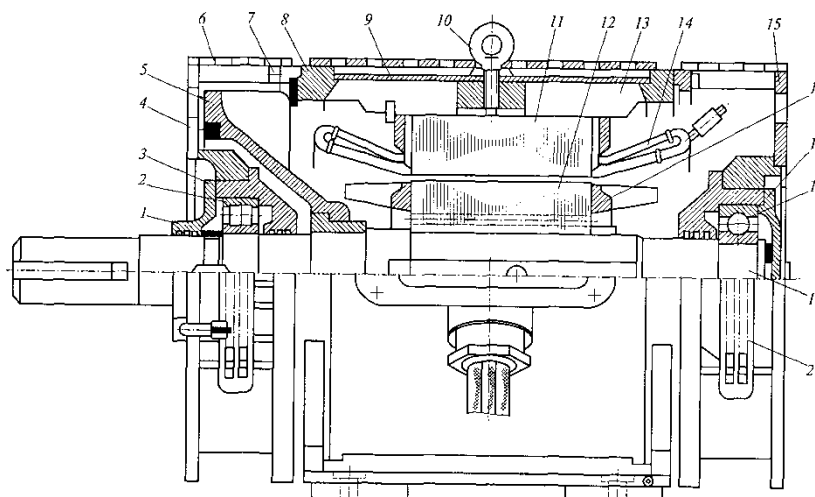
Асинхронный двигатель АЭ92-402.
